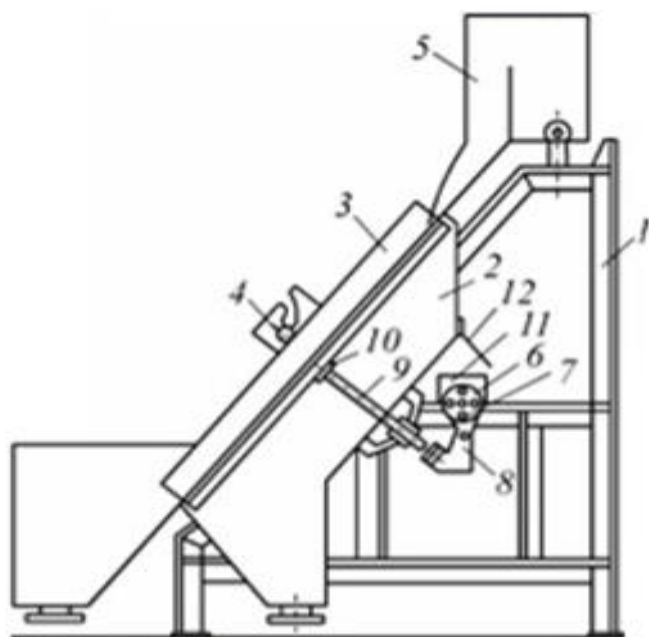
Гідравлічний грохот з незануреною поверхнею [17]: 1 – рама грохоту; 2 - короб; 3 - сито; 4 – кріплення грохоту; 5 – живляча коробка; 6 – вал струшуючого механізму; 7 – струшуючий механізм; 8 – молоток; 9 – шток; 10 – плита; 11 – привод струшуючого механізму; 12 – захисний козирек
